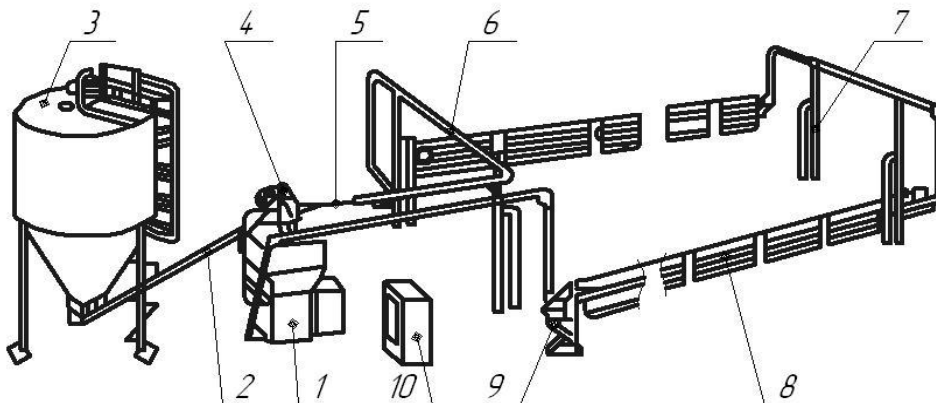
Структурна схема шайбового кормороздавача КШ-0,5: 1 - привод; 2 - завантажувальний шнек; 3 - бункер-накопичувач; 4 - горловина; 5 - шайбовий канат; 6 - кормопровід; 7 - стояк; 8 - дозатор; 9 - привод дозатора; 10 - шафа керування
